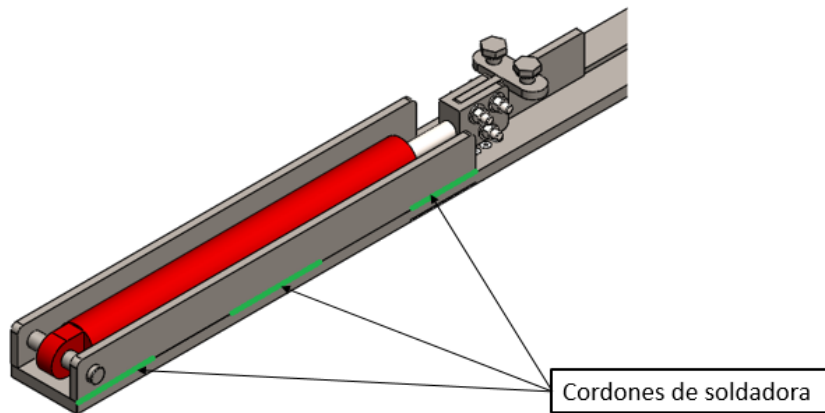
Cordones de soldadura planchuela carro cilindro-refuerzo/vínculo cilindro.
